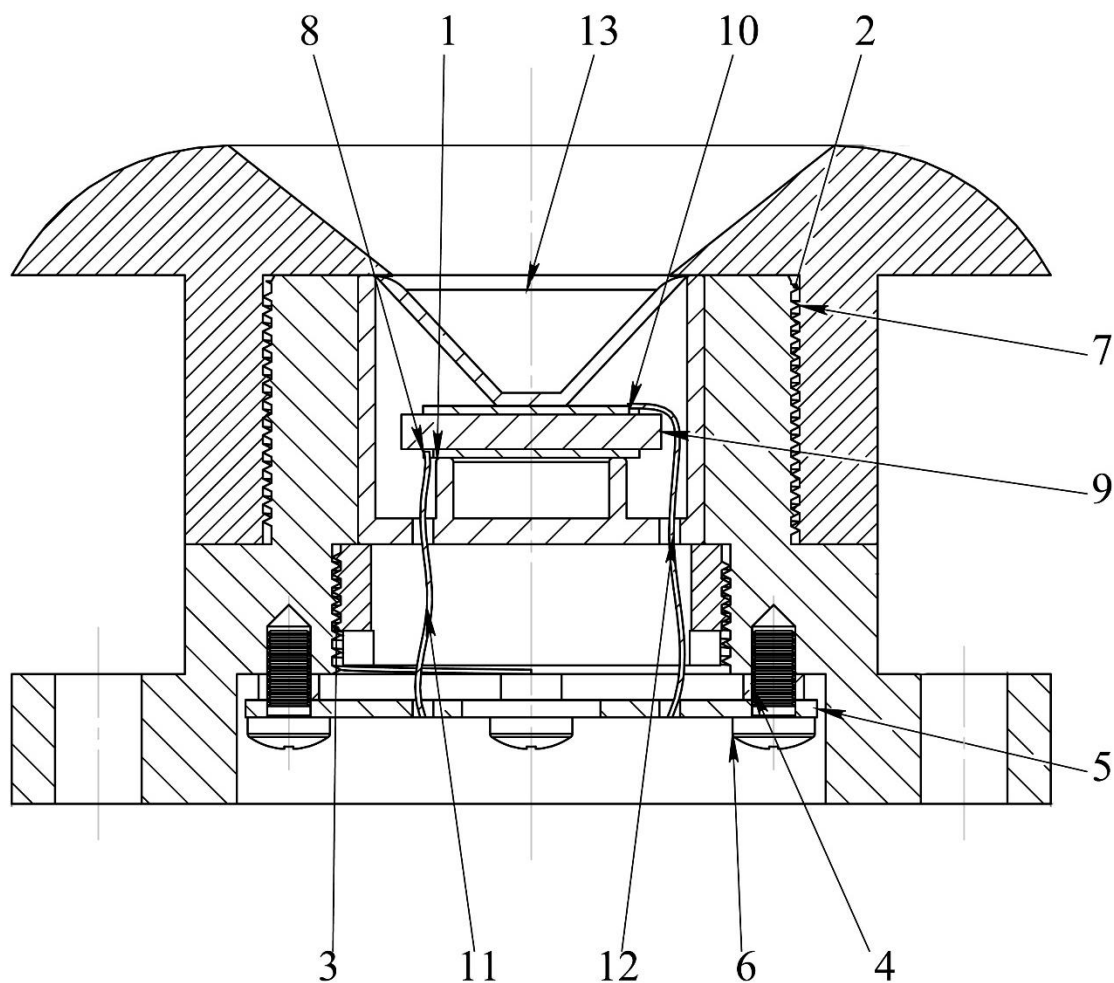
Креслення п'єзоелектричного датчика та корпусу
